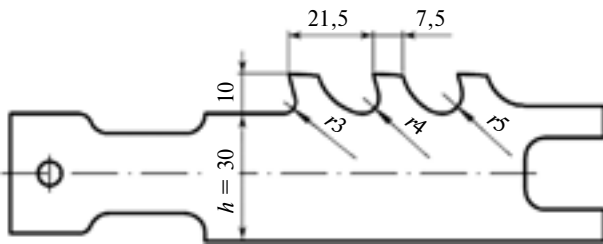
Чертеж модели шпоночной протяжки с основными размерами
